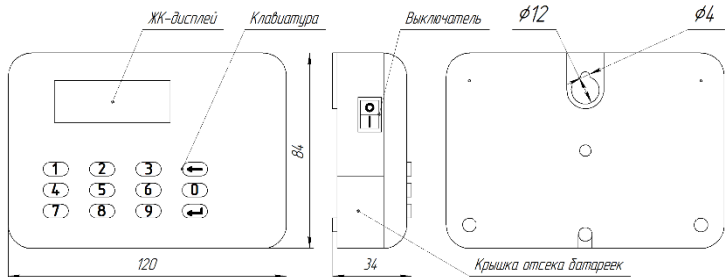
Размеры и основные элементы индикаторного устройства
